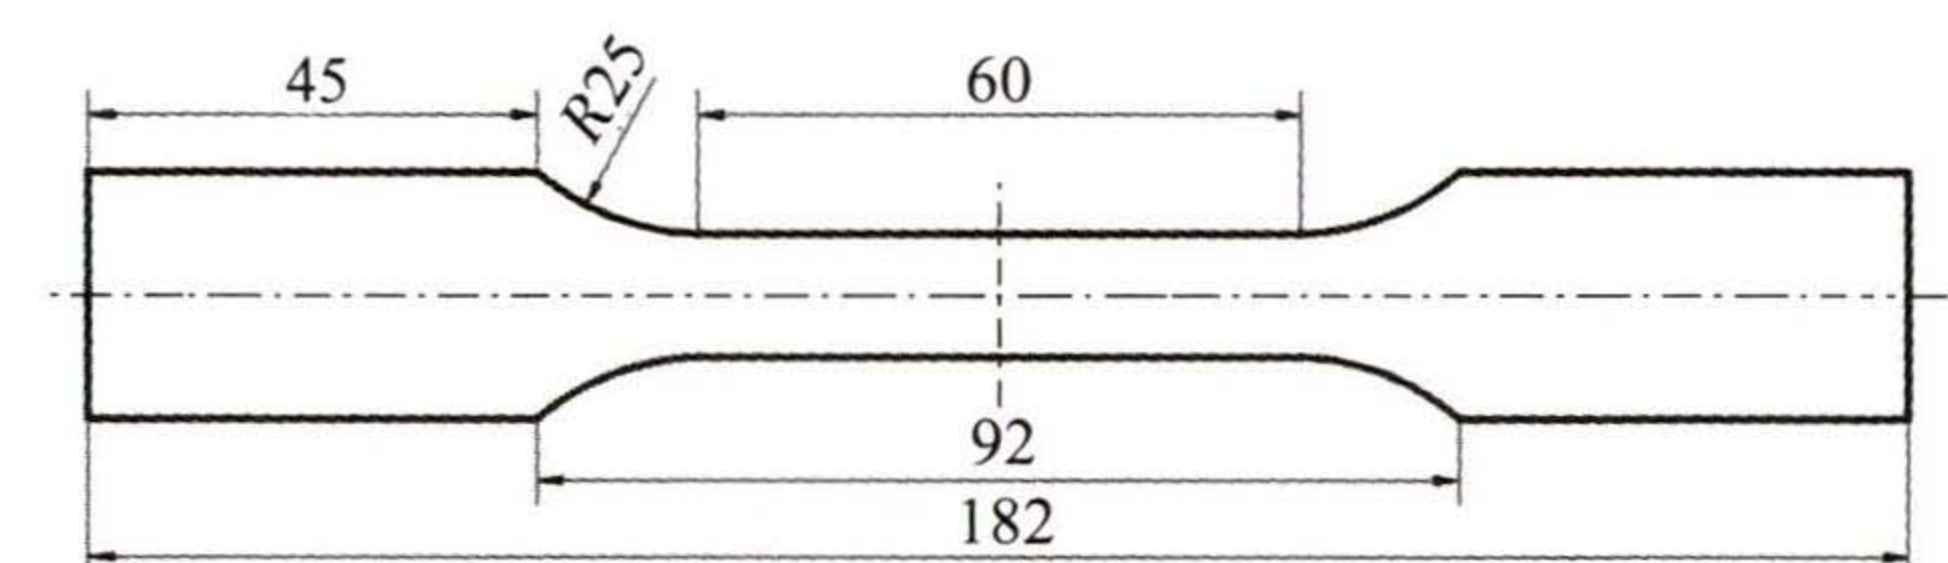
焊接接头拉伸试样尺寸(mm)
